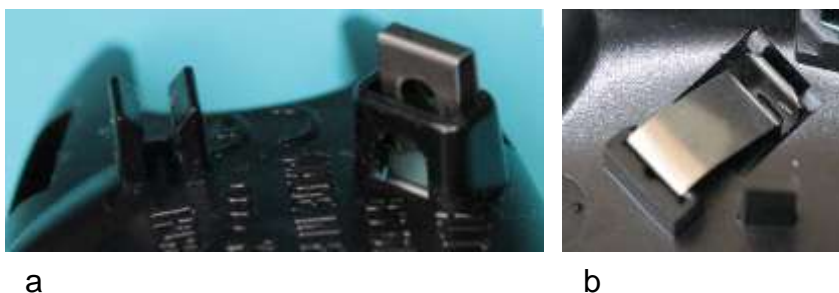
Gestaltung des Bodens: a) Klemmbacken für den Stecker der Masseverbindung, b) Auf der Innenseite des Bodens eingehakte Spannung führende Blattfeder
